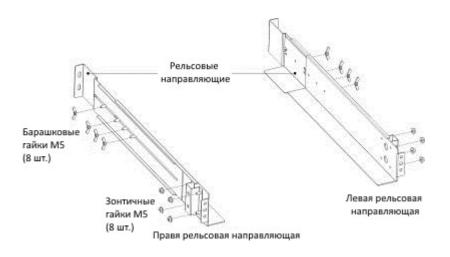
Установка и регулировка рельсовых направляющих
